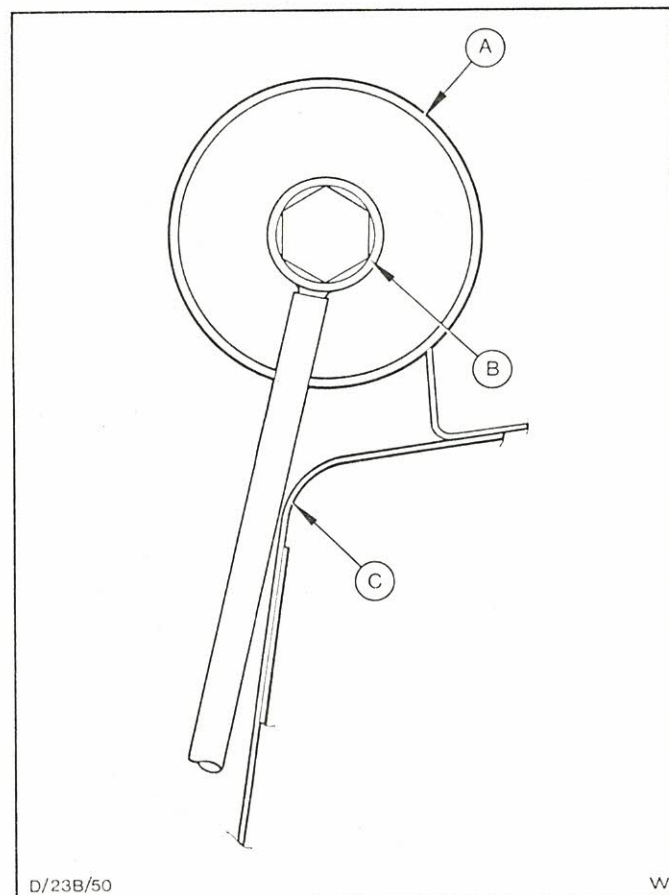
Einbaulage der Kraftstofffilter-Ablaufleitung
